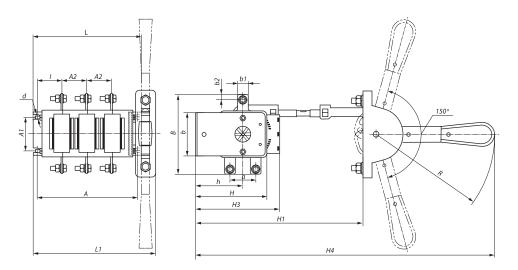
Выключатель-разъединитель универсальный трехполюсный на два направления с д/г камерами, передняя смещенная несъемная левая/правая рукоятка
